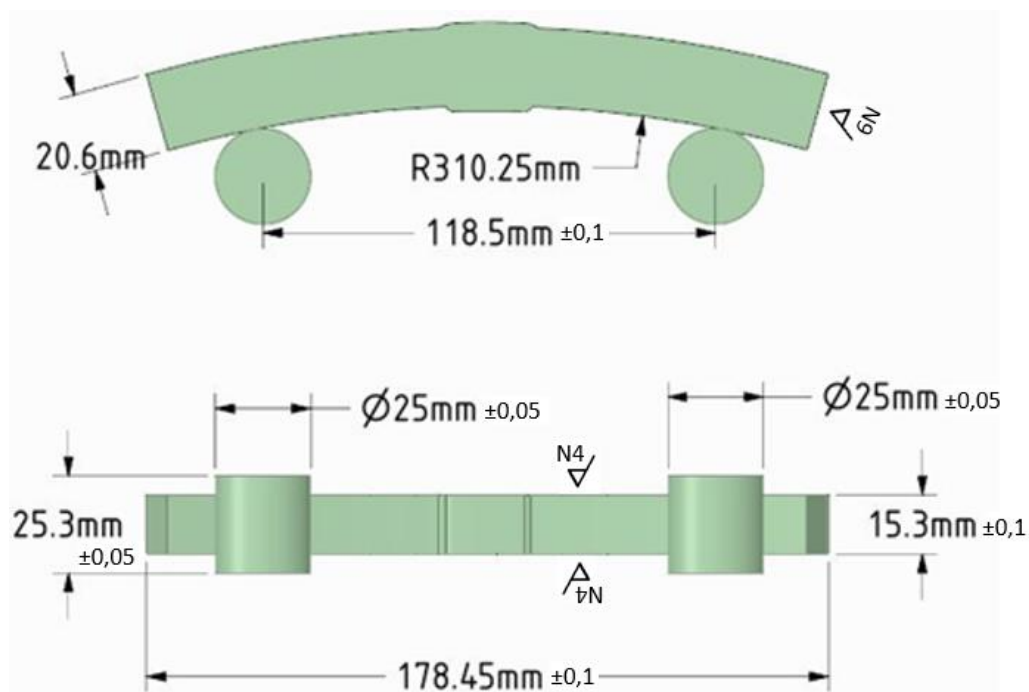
12 - Dimensional dos corpos de prova de flexão
